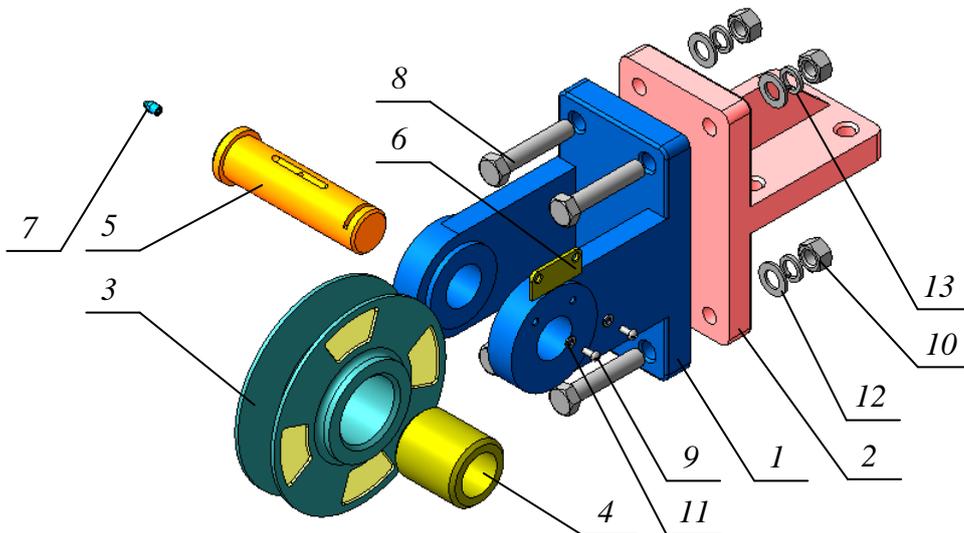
Трехмерная модель сборочного узла «Блок направляющий» в разнесенном виде: 1 – вилка; 2 – кронштейн; 3 – ролик; 4 – втулка; 5 – ось; 6 – планка; 7 – масленка; 8 – болт М18×90 ГОСТ 15589–70 (4 шт.); 9 – винт М6×14 ГОСТ 17473–80 (2 шт.); 10 – гайка М18 ГОСТ 5927–70 (4 шт.); 11 – шайба 6 ГОСТ 11371–78 (2 шт.); 12 – шайба 18 ГОСТ 11371–78 (4 шт.); 13 – шайба 18 Н ГОСТ 6402–70 (4 шт.)
